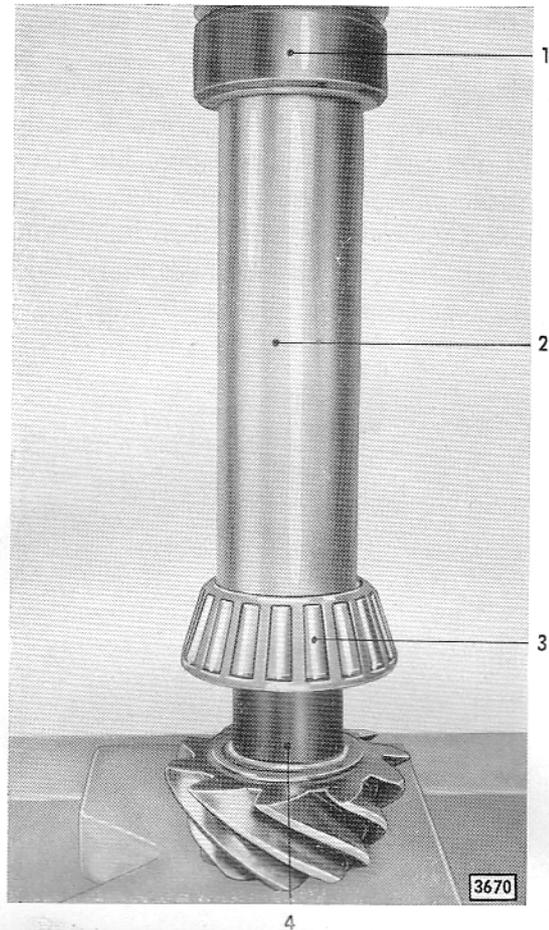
Inneren Laufring mit Kegelkäfig des inneren Lagers auf Antriebskegelrad aufpressen
